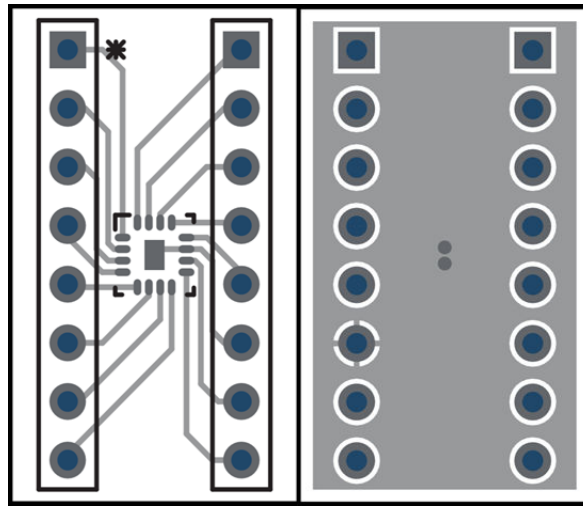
RTE 封装顶层 (左) 和底层 (右) 的 PCB 布局
